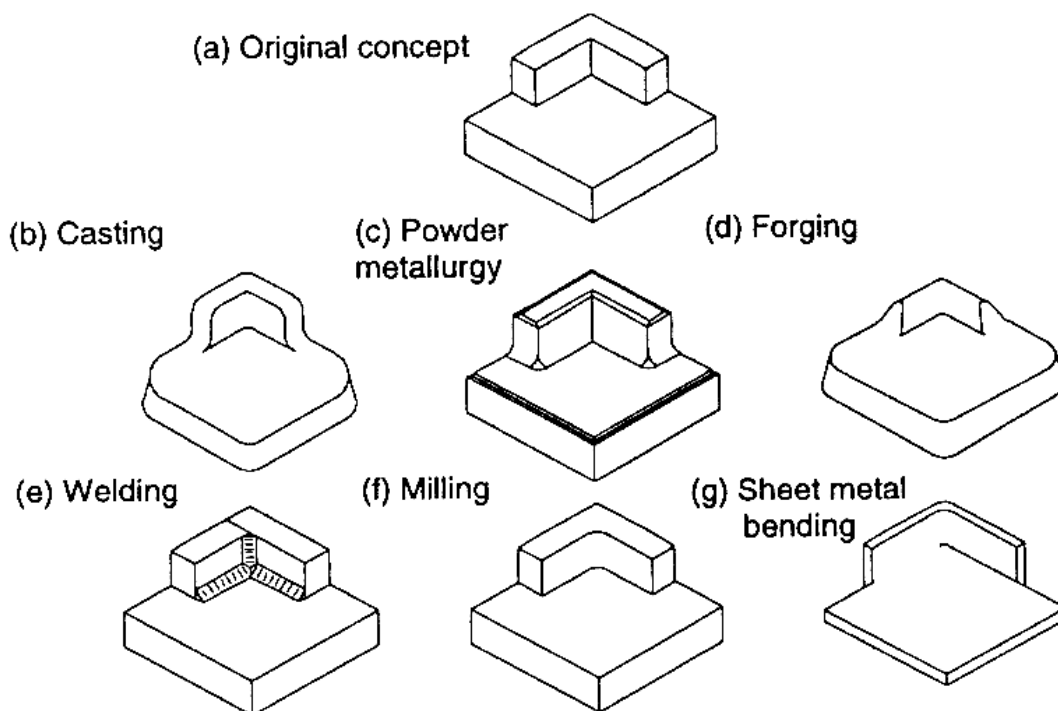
Efeito do processo de manufatura sobre a geometria (detalhes exagerados).
